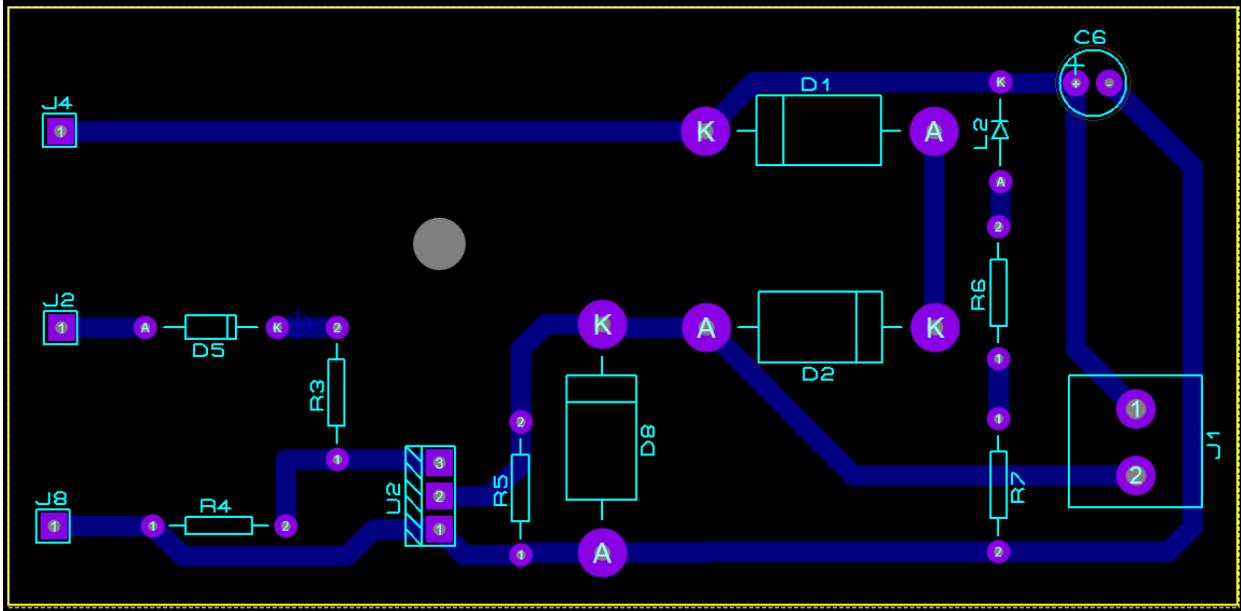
Diseño final parte 1 hecho en PCB layout de proteus
